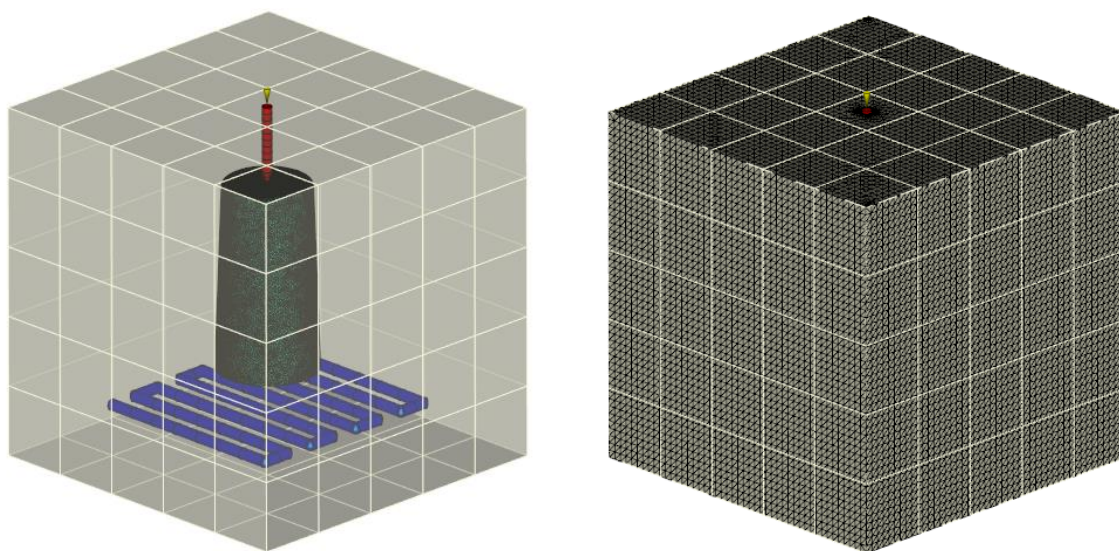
Superfície do molde (esquerda) e superfície do molde com malha aplicada (direita)
